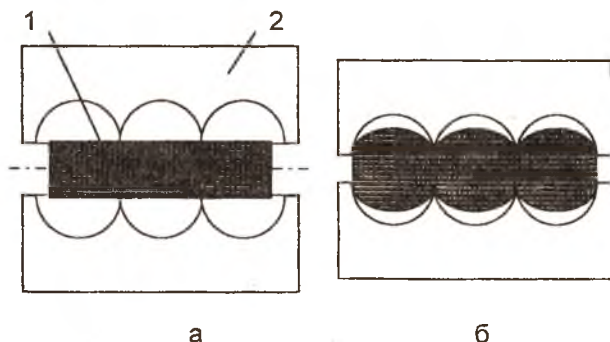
Схема разделения цилиндрической заготовки ножами цилиндрического профиля: 1- заготовка, 2 - ножи; а - положение до рубки; б - внедрение ножей в заготовку
